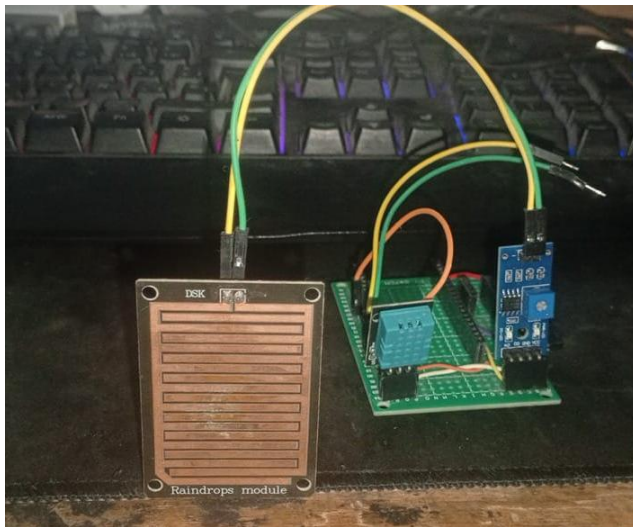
Preparación de la protoboard y soldadura de pines header.
